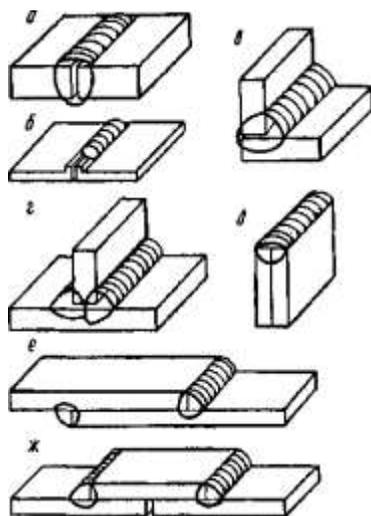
Типы сварных соединений: а – стыковое; б – стыковое с отбортовкой; в – угловое; г – тавровое; д – торцевое; е – нахлестанное; ж – с накладкой
